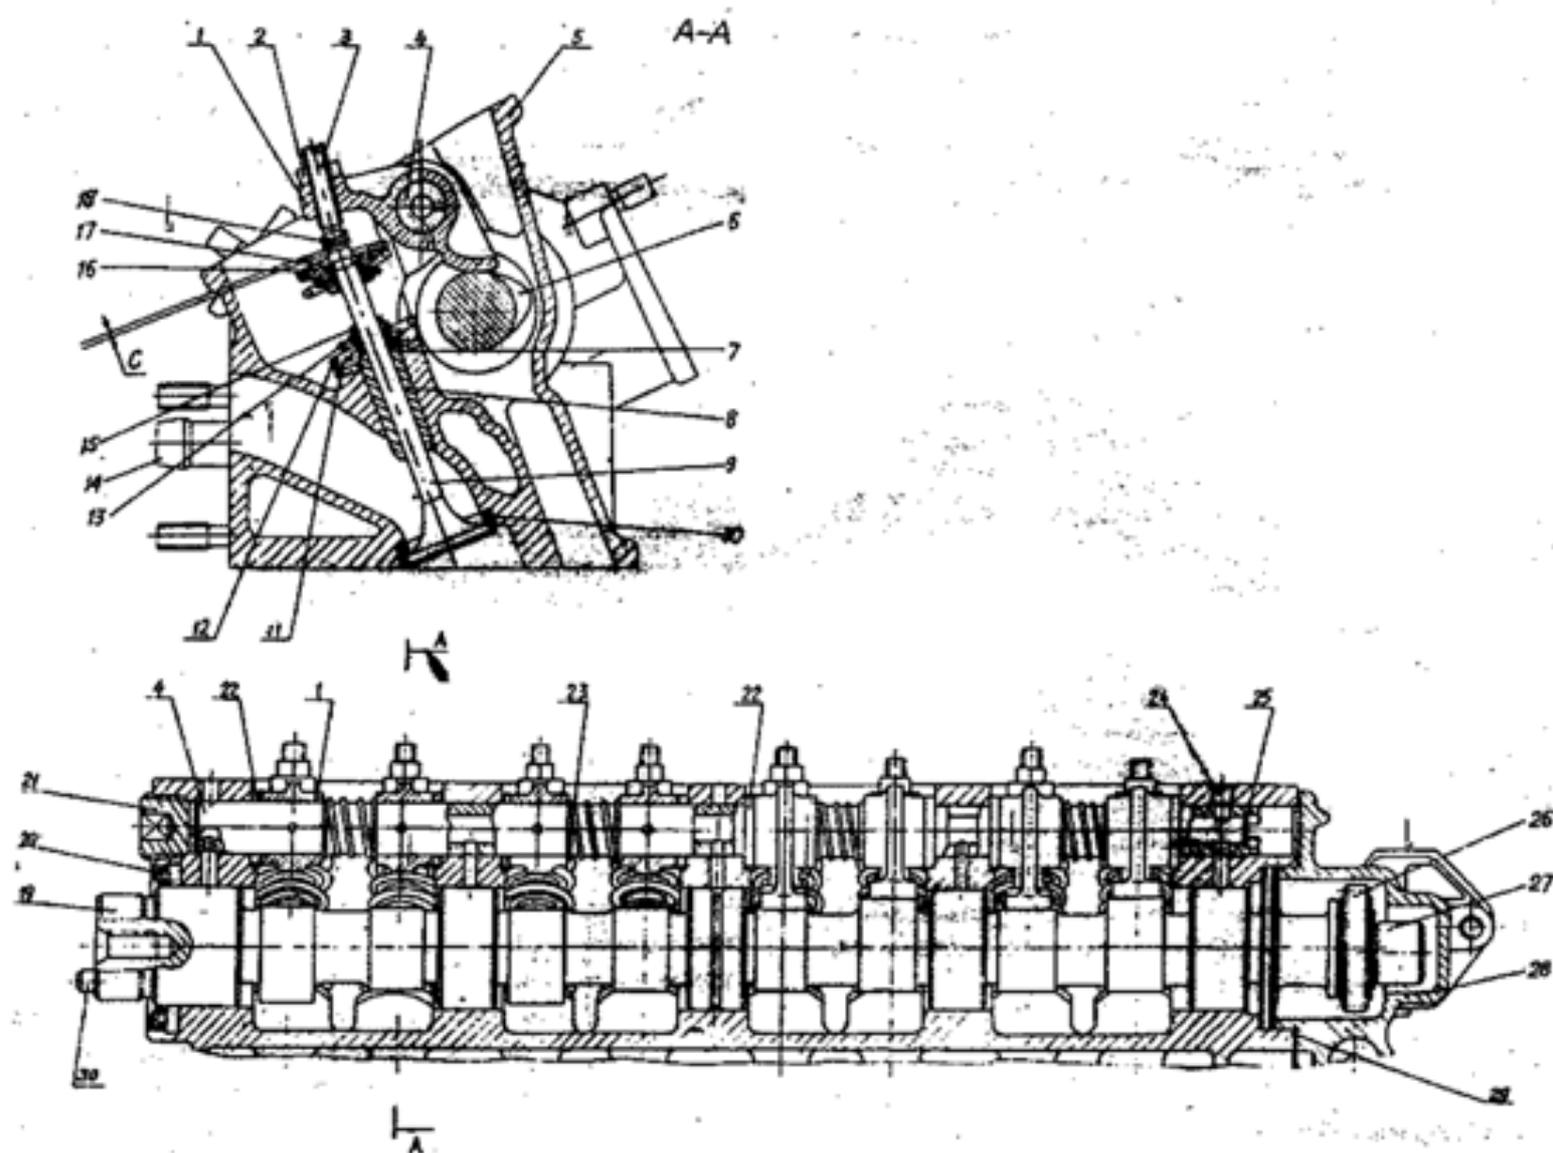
Головка цилиндров и схема регулировки зазоров в механизме привода клапана: 1 - коромысло; 2 - гайка; 3 - регулировочный винт коромысла клапана; 4 - ось коромысел; 5 - головка цилиндров; 6 - кулачок распределительного вала; 7 - кольцо стопорное; 8 - втулка направляющая; 9 - клапан; 10 - седло клапана; 11 - шайба опорная внутренней и наружной пружины; 12 и 13 - пружины наружная и внутренняя; 14 - патрубок; 15 - маслоотражательный колпачок клапана; 16 - тарелка пружины клапана; 17 - сухари тарелки клапана; 18 - наконечник регулировочного винта коромысла; 19 - вал распределительный; 20 - манжета уплотнительная; 21 - пробка; 22 - шайба упорная; 23 - пружина оси коромысел; 24 - винт стопорный; 25 - заглушка масляного канала; 26 - шестерня привода датчика-распределителя ведущая; 27 - кулачок привода бензинового насоса; 28 - корпус привода датчика-распределителя и бензинового насоса; 29 - прокладки; 30 - штифт; С - зазор для клапанов: впускных 0,13...0,17 мм, выпускных 0,28...0,32 мм
